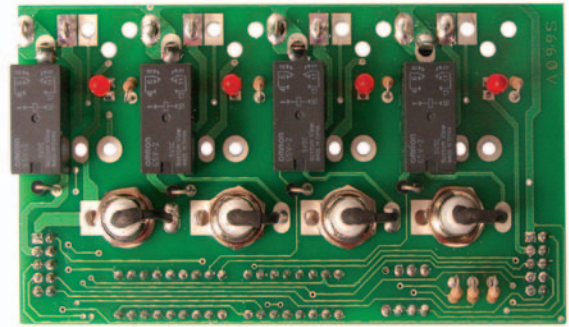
Photo d'un des prototypes de la platine de la section Vidéo du commutateur vidéo, côté soudures (relais).
